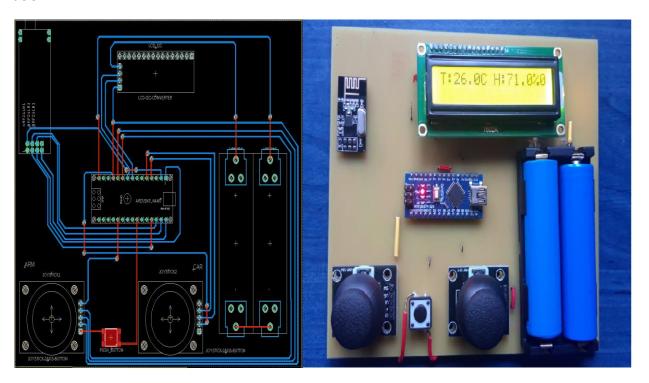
Schema layout PCB Telecomandă; Fig.3 Cablajul proiectat și asamblat
